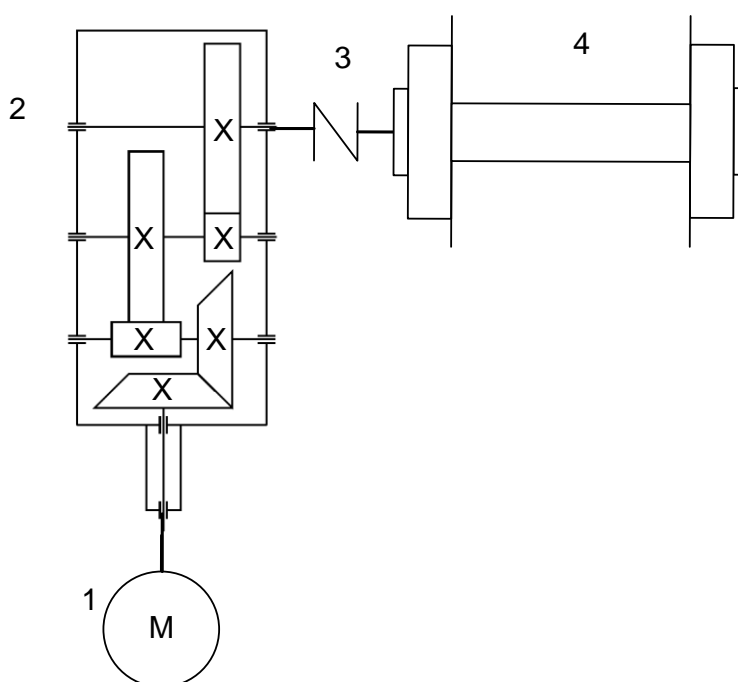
Кинематическая схема механизма передвижения передаточной тележки
